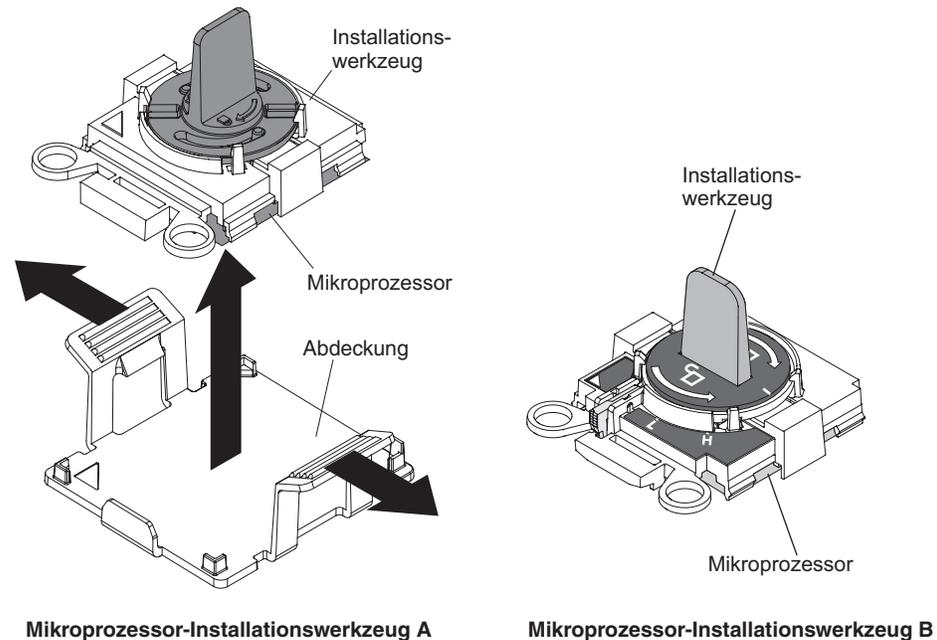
Installationswerkzeuge für Mikroprozessoren
